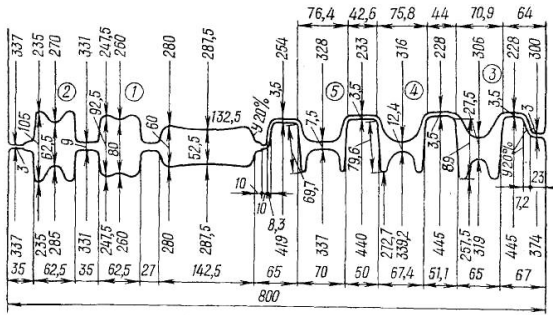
Профиль валков для прокатки заготовки двутавровой балки
